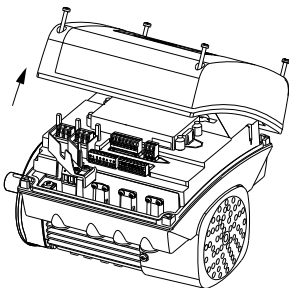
Desmontaje de la cubierta de la caja de conexiones
